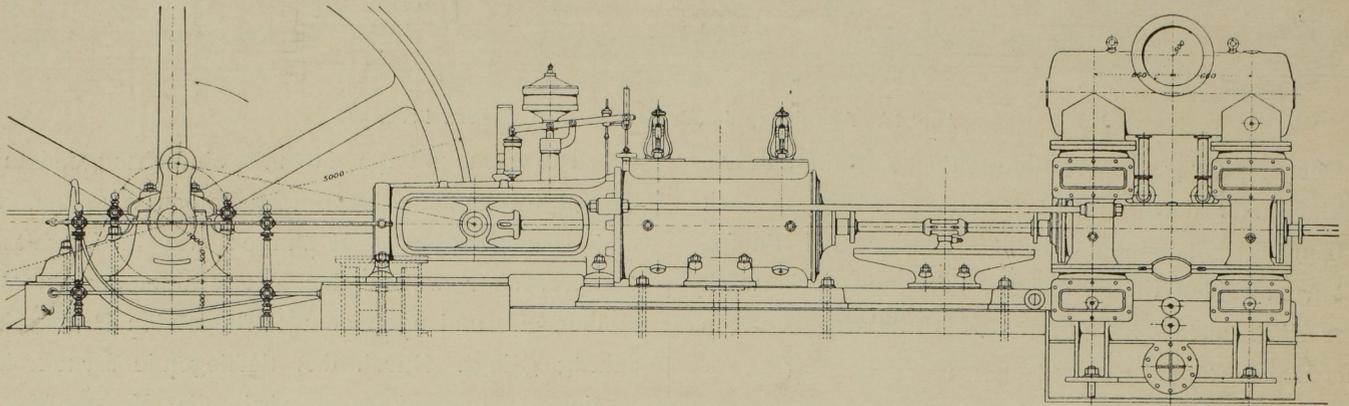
Seitenansicht der Pumpmaschine. Massst. 1 : 60.
